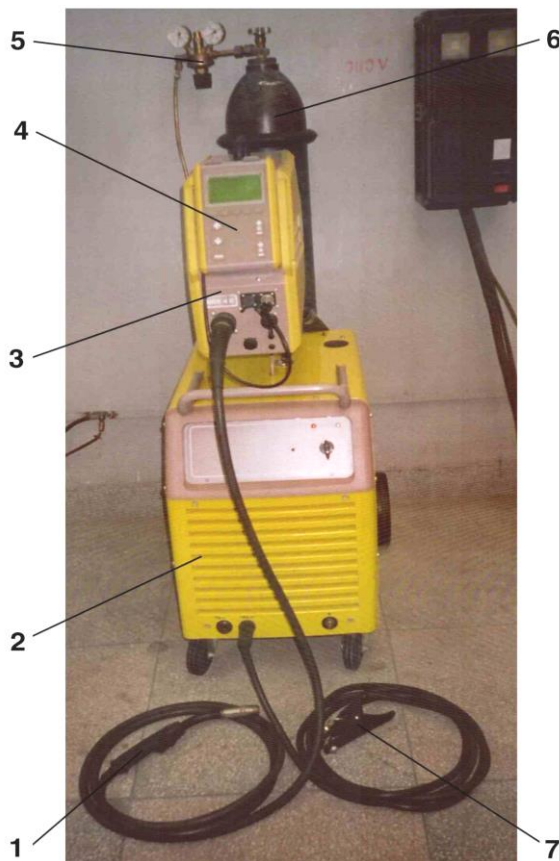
Sursă de sudare universală Aristo Lud 320: 1- pistol de sudare; 2- redresor de sudare; 3- mecanism de avans sârmă electrod MEK 4C; - pupitru electronic de comandă PUA 1; 5- reductor de presiune cu debitmetru; 6- butelie gaz protecție; 7- clemă de masă [22]
